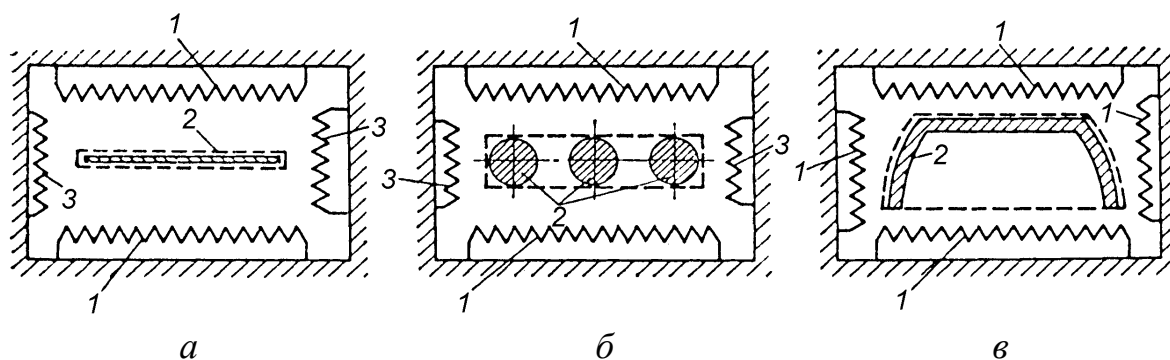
Определение тепловоспринимающей поверхности садки сложной формы: *а* — тонкая пластина; *б* — составная садка; *в* — отливка. *1* — основные нагреватели; *2* — нагреваемые изделия; *3* — нагреватели для компенсации только тепловых потерь через стенки
